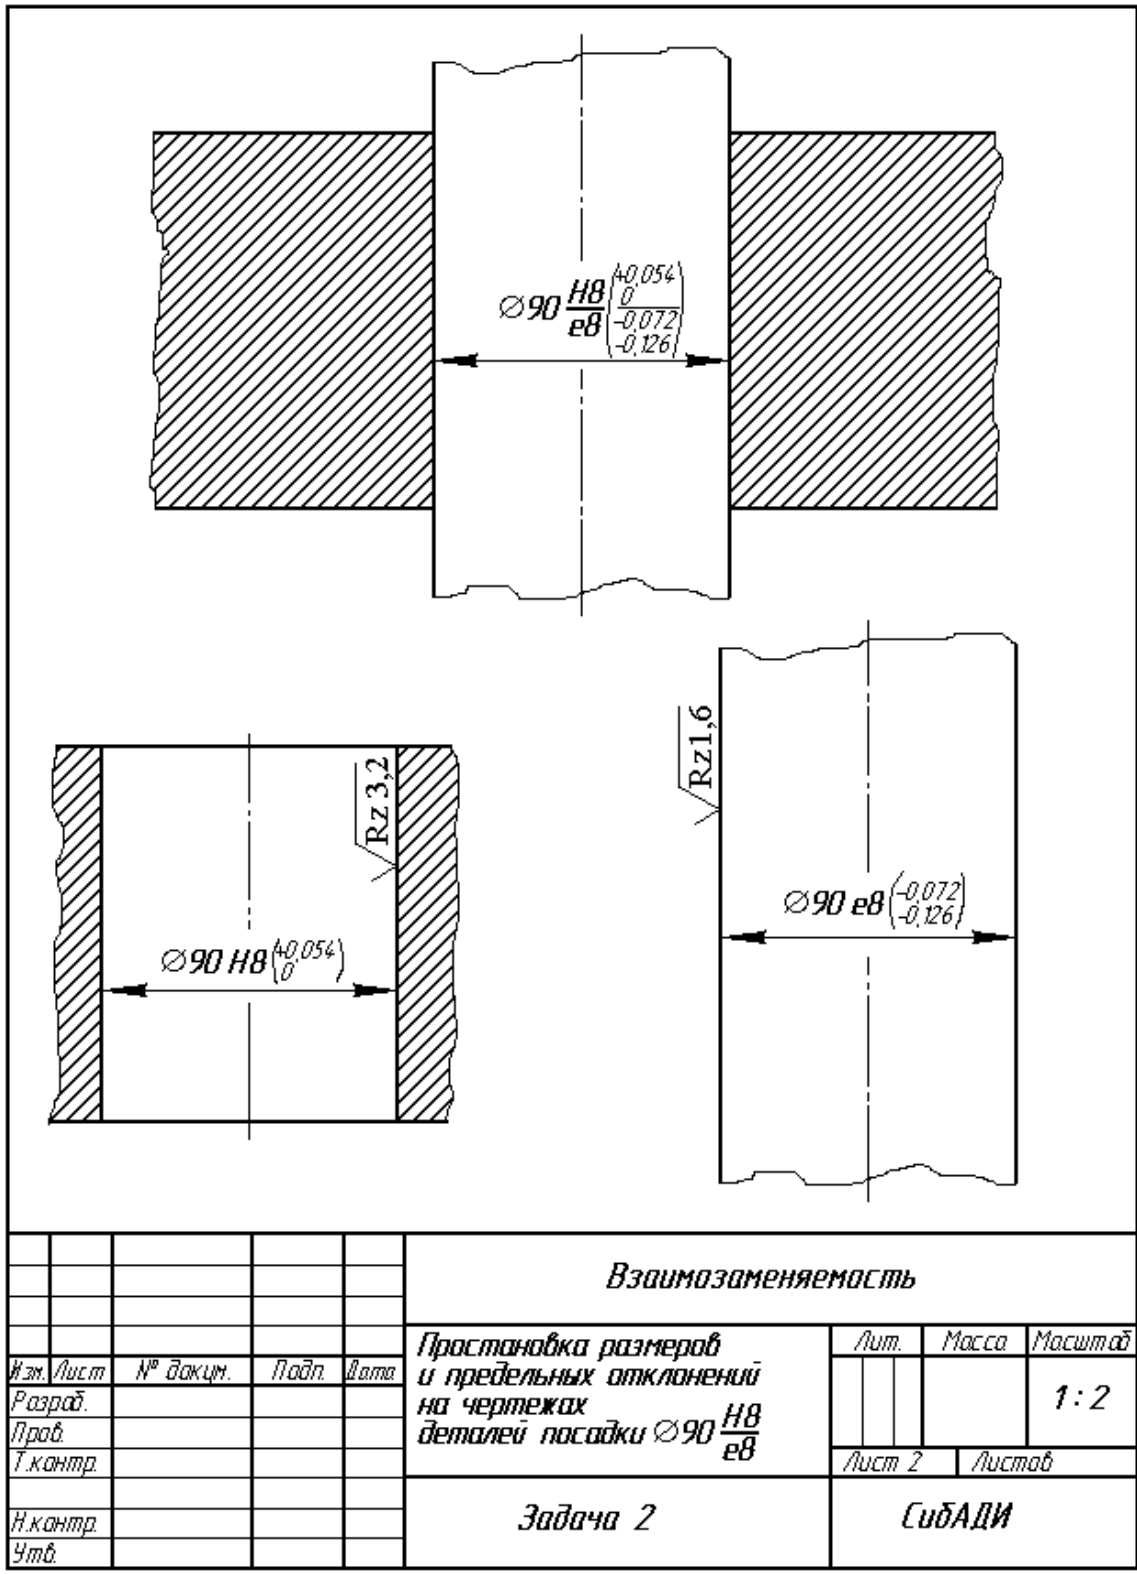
Простановка размеров и отклонений деталей подшипника скольжения
